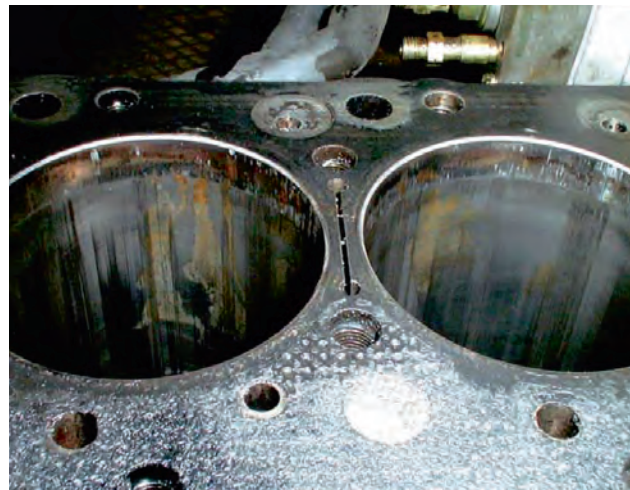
Diámetro interior de cilindro con estrías longitudinales
